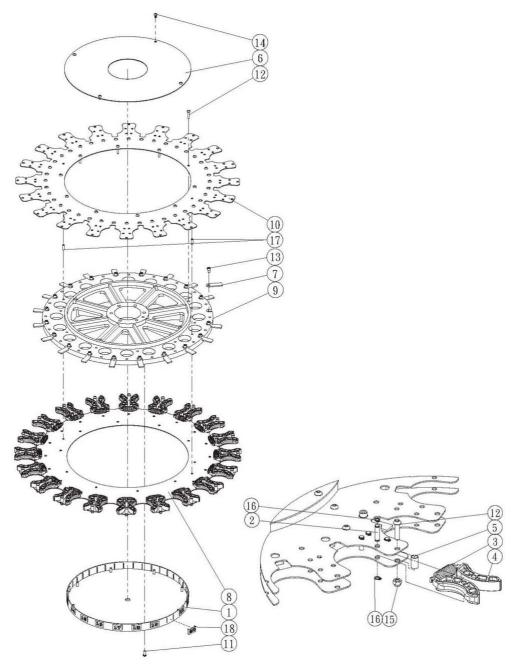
Werkzeugwechsler 3-4 -Tool changer 3-4
